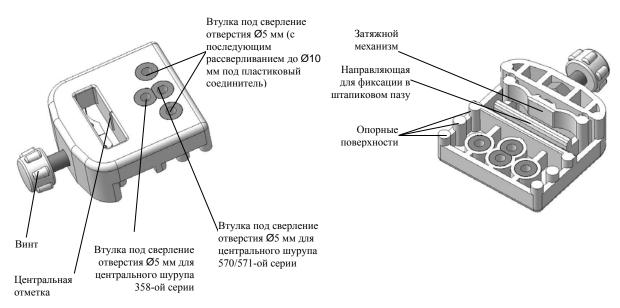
КСИ 358/570/571 Кондуктор соединителя импоста.
